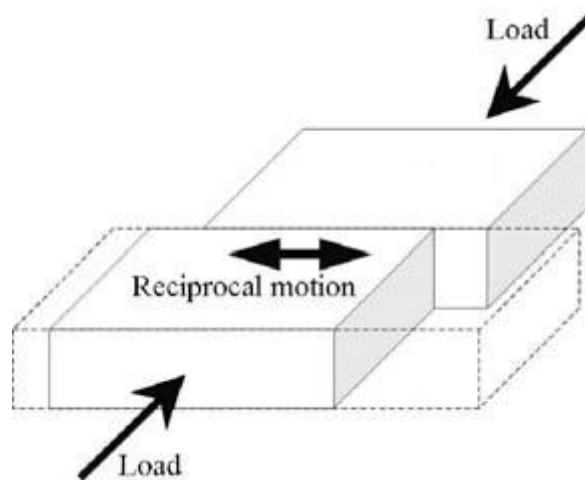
Illustrazione schematica del processo di linear friction welding [19].
